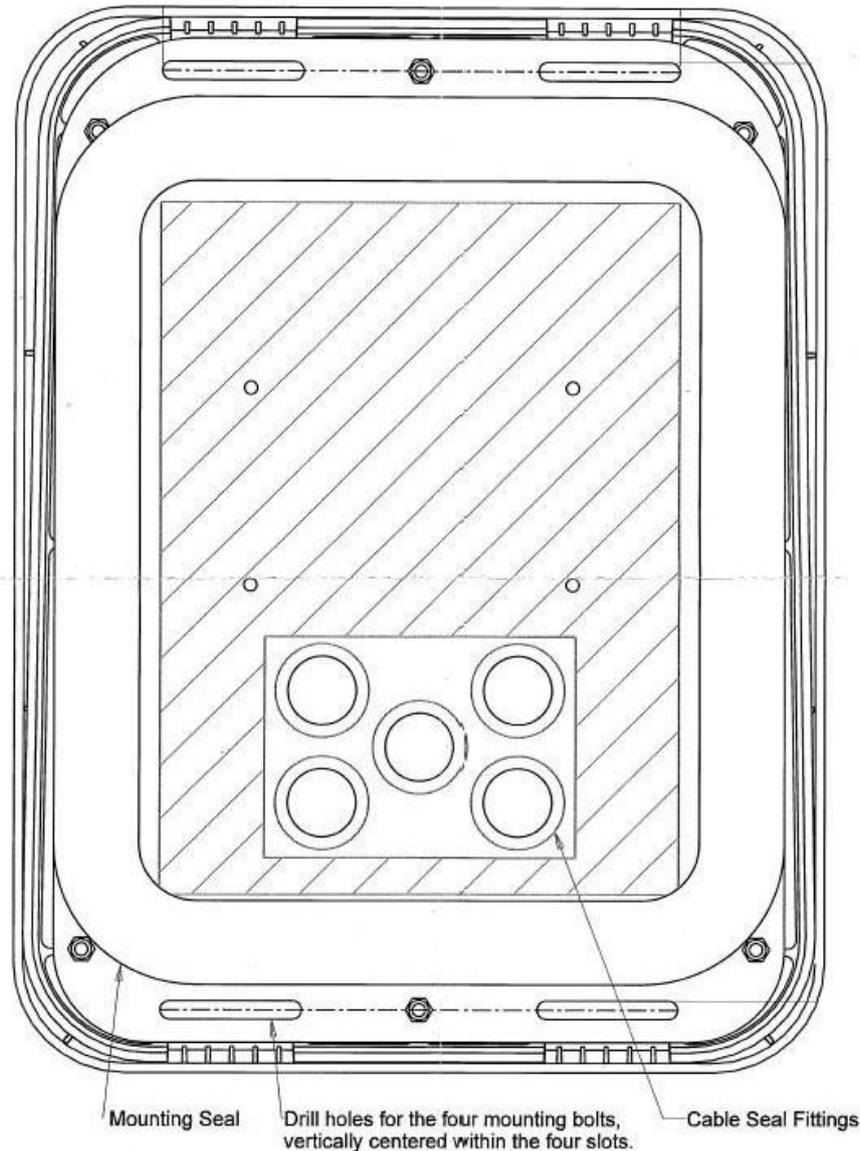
MorphoAccess® Série OMA500 – Vue arrière
